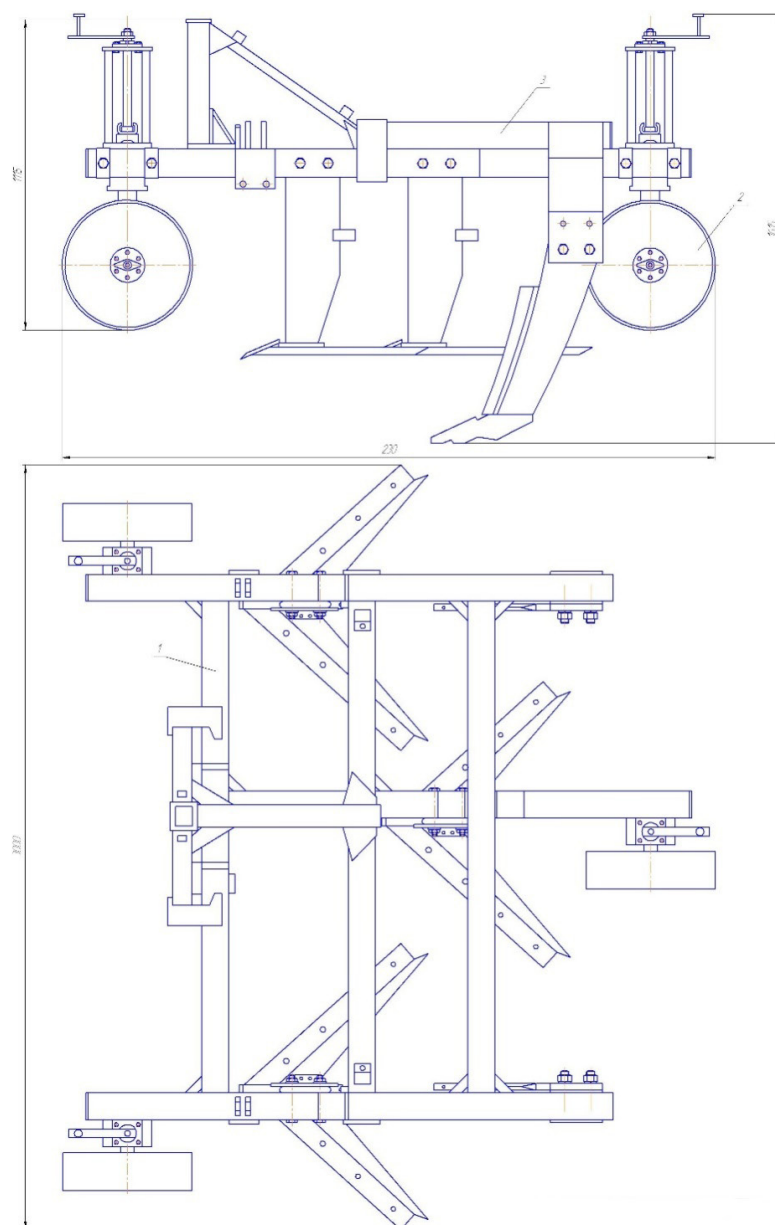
Вид общий плоскореза-глубокорыхлителя с почвоуглубителями ПГ-3
